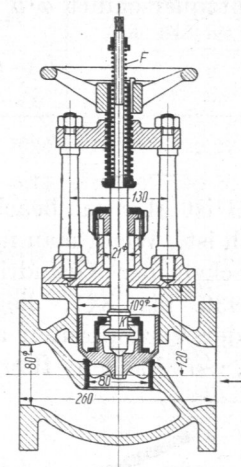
Rohrbruchventil (Klein, Schanzlin und Becker). M. 1:10.
